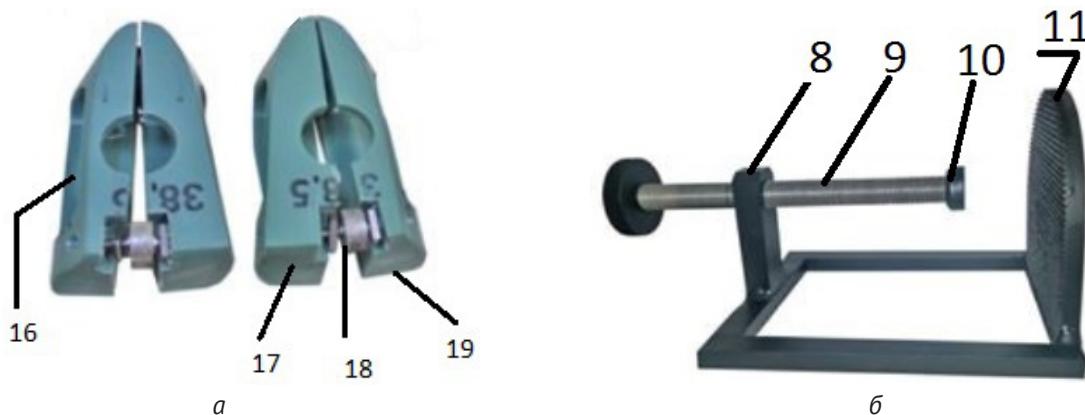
Приспособления для закрепления обуви: а – вкладыши в пяточную часть обуви для левой и правой полупар; б – приспособление для закрепления полупары обуви
